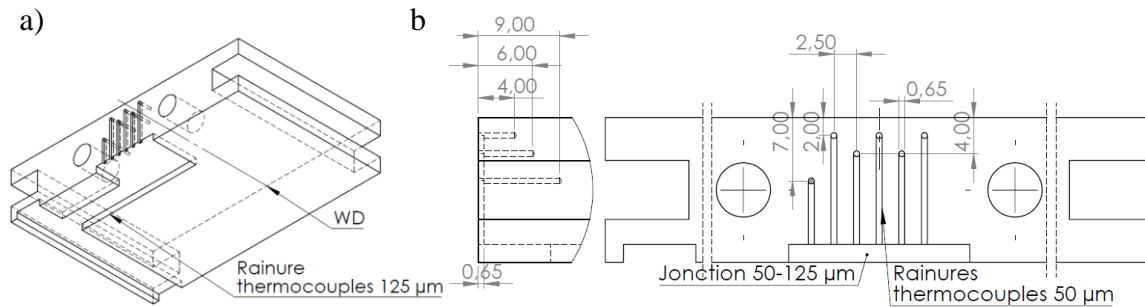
a) usinage d'une portion de l'enclume, b) vue détaillée de l'usinage destiné au passage des thermocouples
